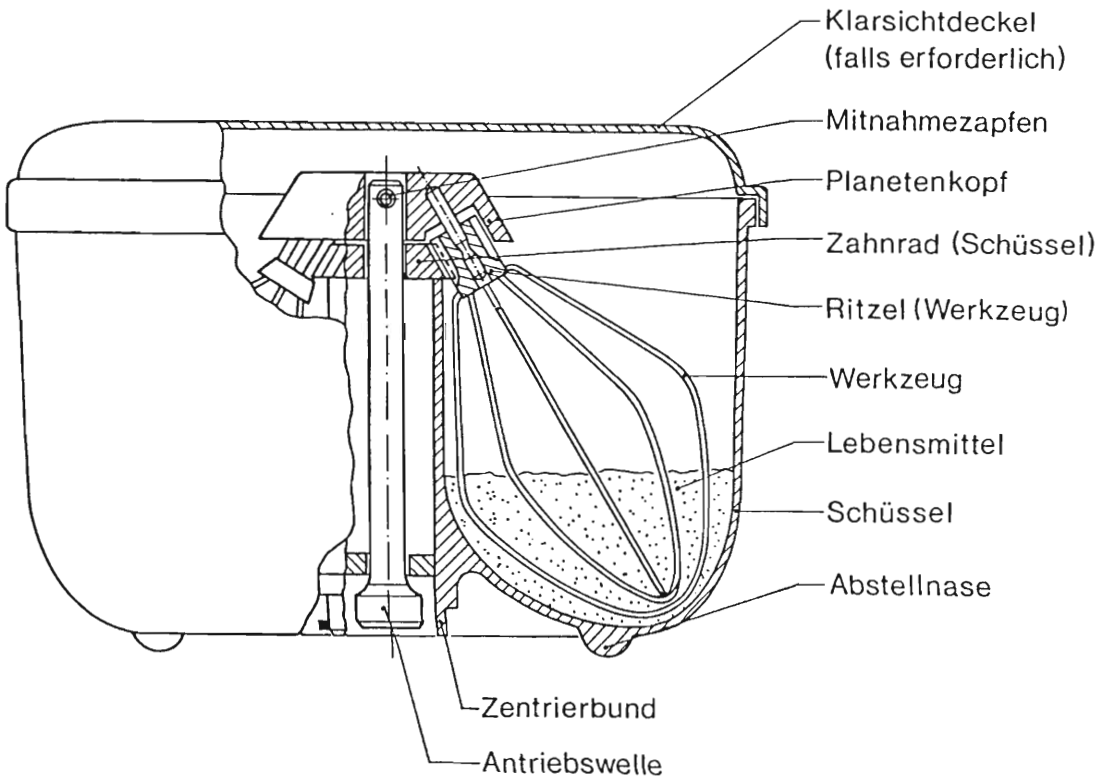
/18: Rührwerkzeuge mit Schüssel einer Stand-Küchenmaschine (Vertikal-Teilschnitt)
